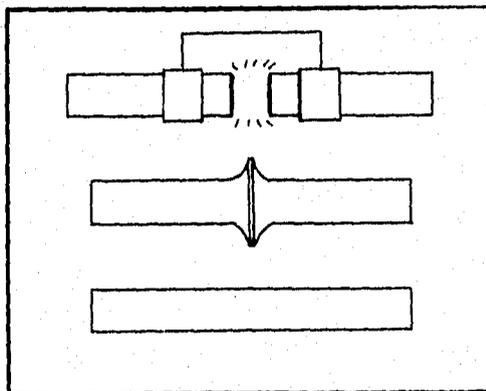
ESQUEMA DE SOLDADURA POR FLASH O CHISPEO.
